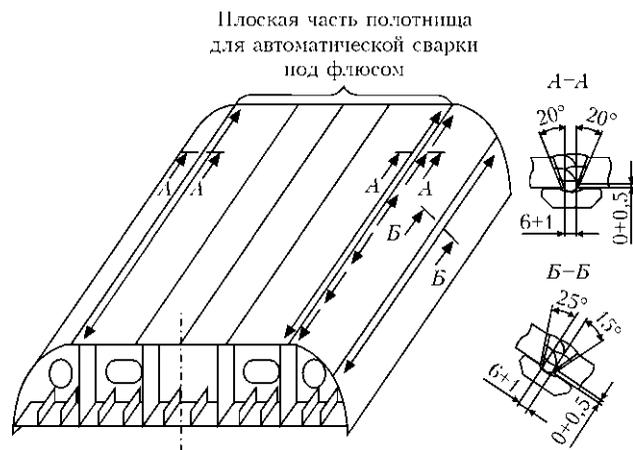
Схема сварки внешней обшивки днищевых секций судна: длинная стрелка — направление сварки пазов; короткая — корневых проходов швов на ФКП
